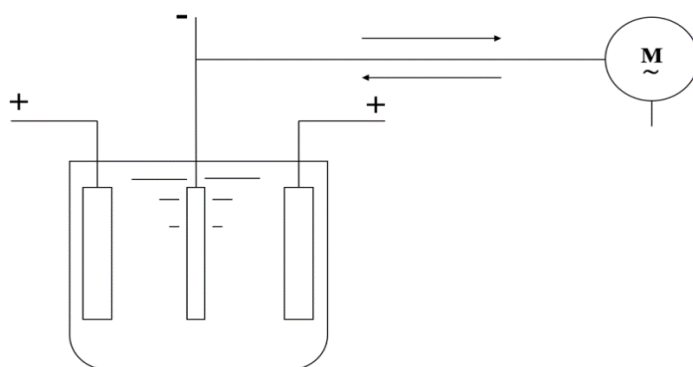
Схема горизонтального покачивания катодной штанги
